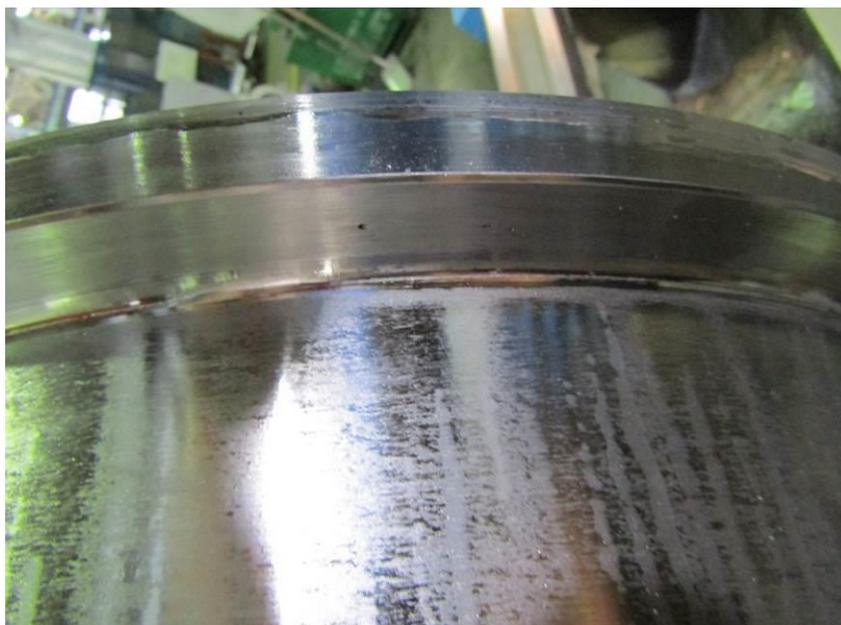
Дефекты на наплавленной поверхности колеса
